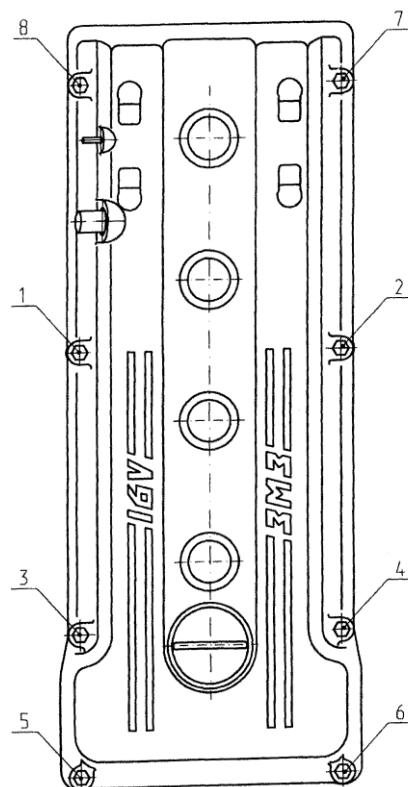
Последовательность затяжки болтов крепления крышки клапанов
